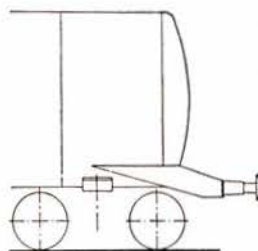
c Zweiachsiger Kesselwagen mit Aluminiumkessel für technische Fette und Ladegüter, die auf Stahl einwirken.
